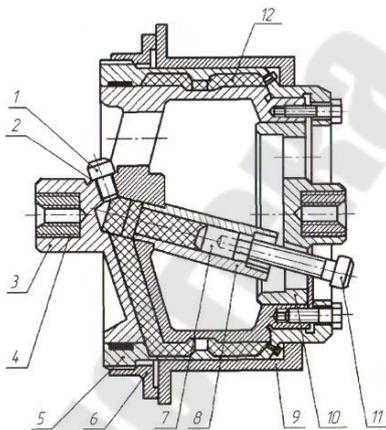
Оправка с гидропластовым зажимом для наружного шлифования: 1, 11 – винт; 2 – прокладка; 3 – корпус; 4 – 6 – втулки; 7 – плунжер; 8 – цилиндр; 9 – заготовка; 10 – шайба; 12 – гидропласт
